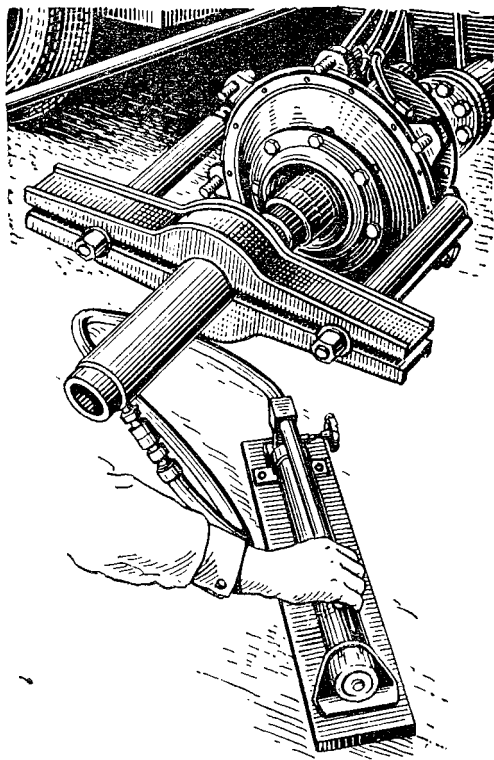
Спрессовка ступицы колеса универсальным приспособлением УК-2А и гидравлическим прессом ГП-20
